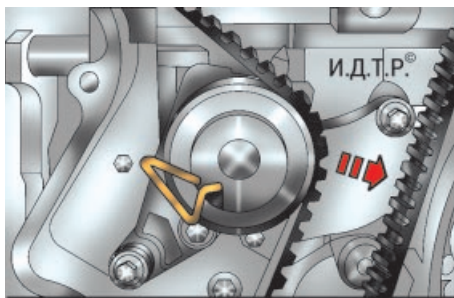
Ослабление натяжения ремня привода газораспределительного механизма
